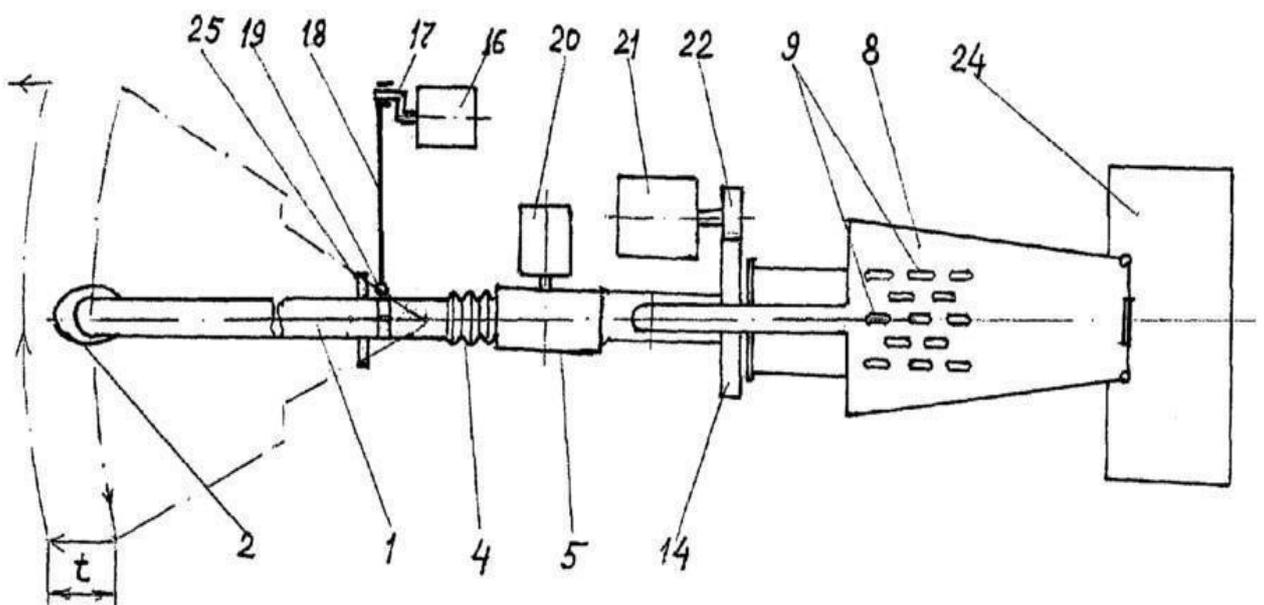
Схема листоподборщика (вид сверху)
